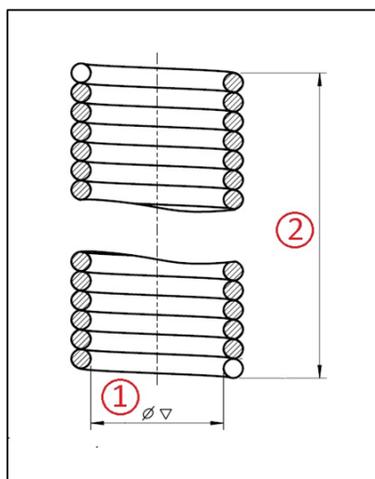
Desenho de molas do tubo – Fonte: Empresa A
